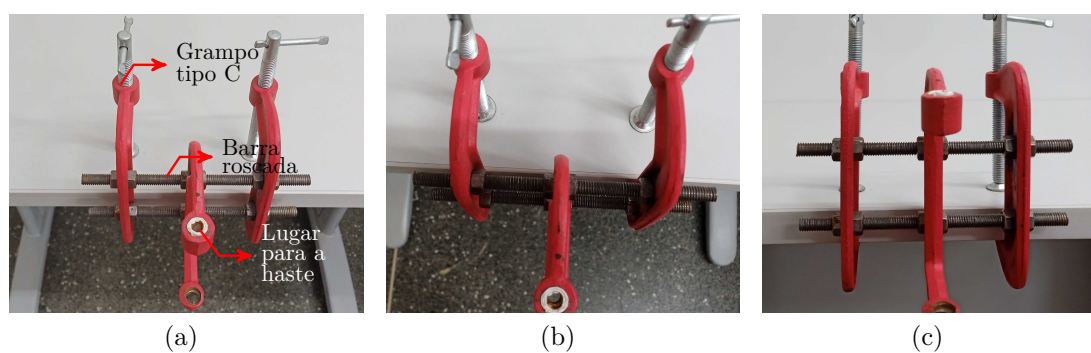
Protótipo do fixador: (a) visão em 3D, (b) visão superior e (c) visão frontal.
